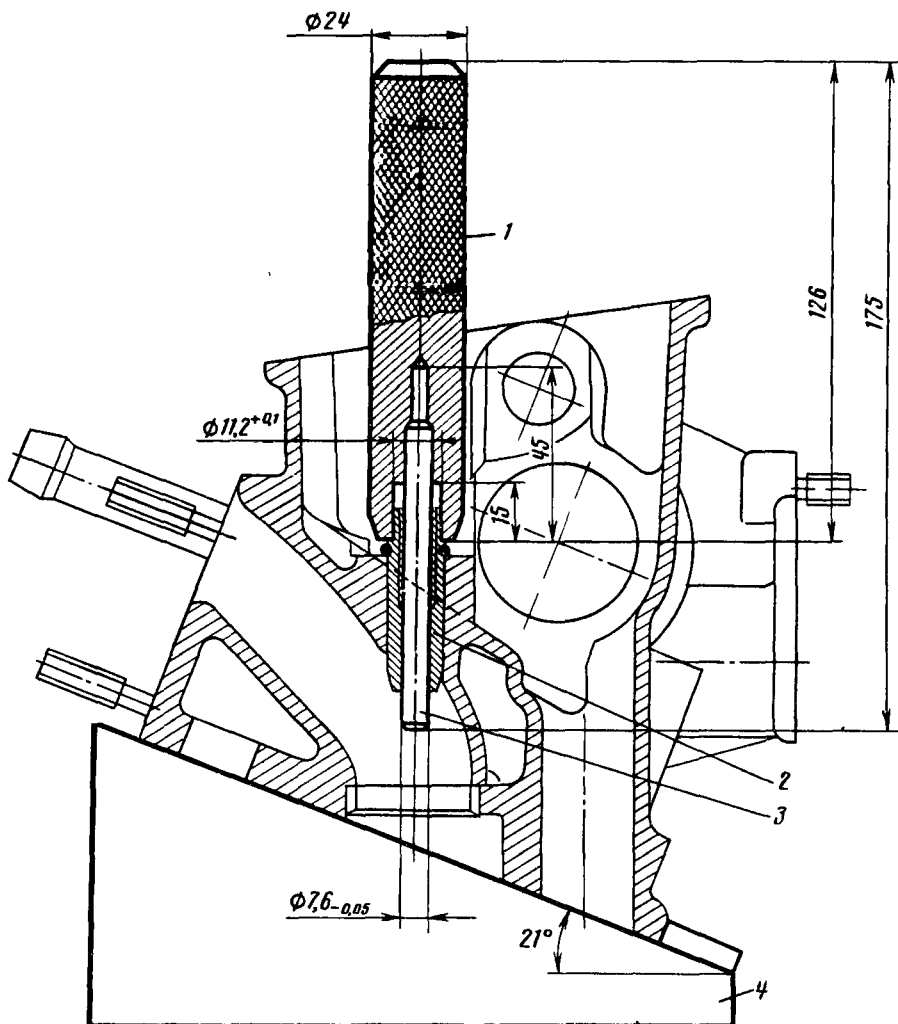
Оправка для запрессовки направляющих втулок клапанов:
